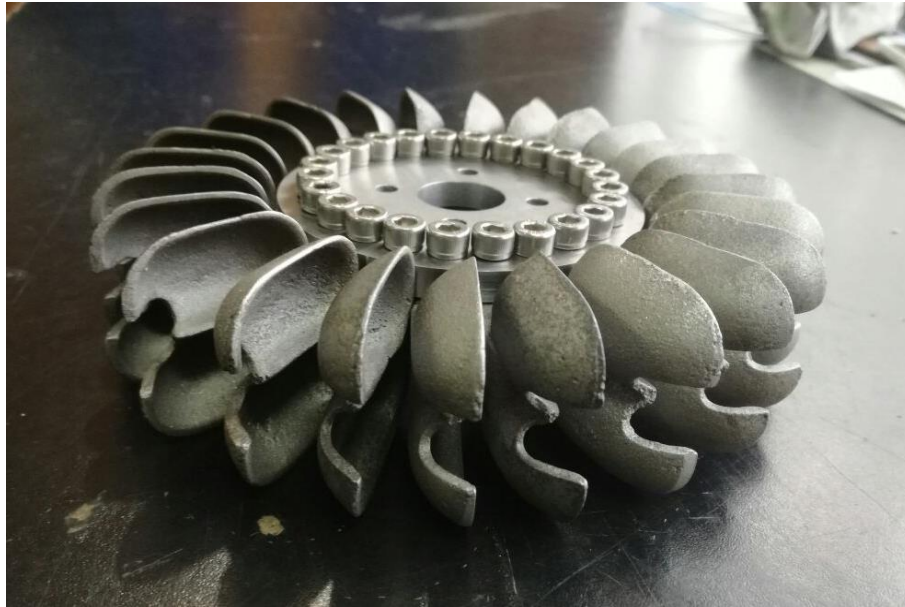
Ensamblaje final del rodete. Fuente: Autores
